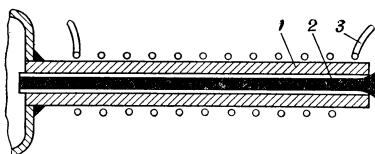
Трубчатый вакуумный накател: 1 — капиллярная трубка; 2 — проволока; 3 — подогреватель (показана его обмотка).
